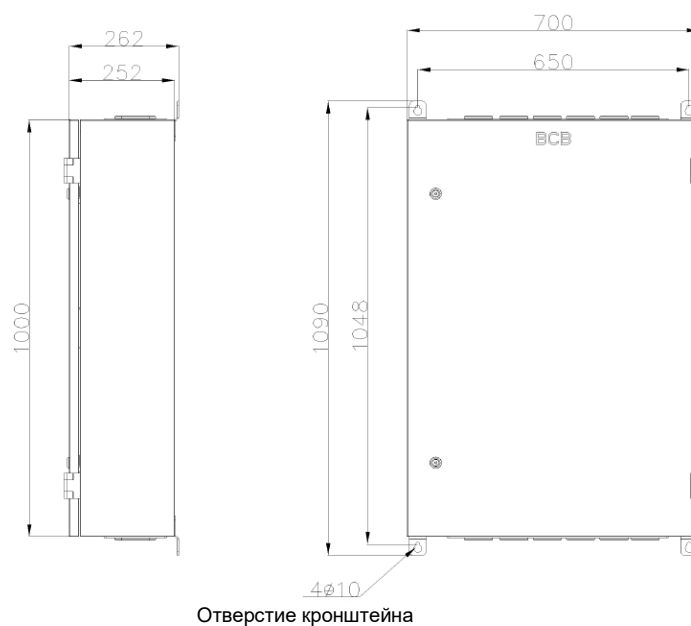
Размеры монтажных отверстий для настенного монтажа батарейного автомата ИБП 250–400 кВА (размеры в мм)
